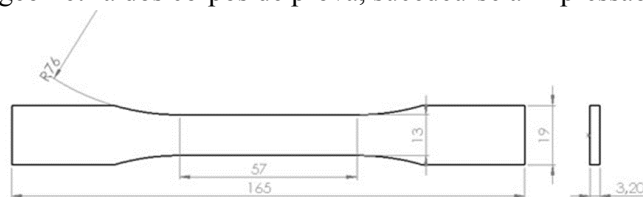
Desenho com dimensões em milímetros dos corpos de prova segundo a norma ASTM-618.
